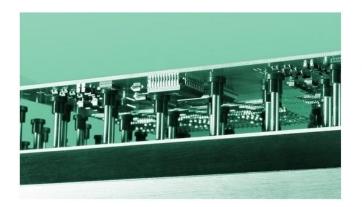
Soporte para PCB; (Surface Mount Process, 2015)
